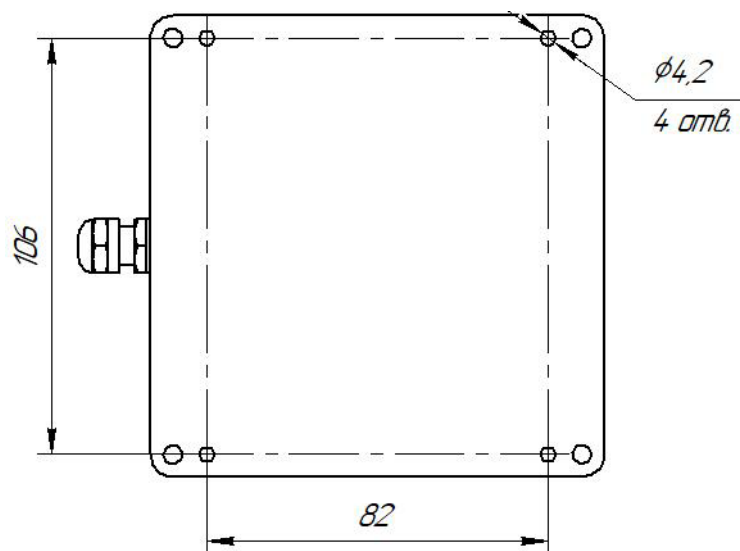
Разметка крепления зонной коробки ЗК-5-Ех
